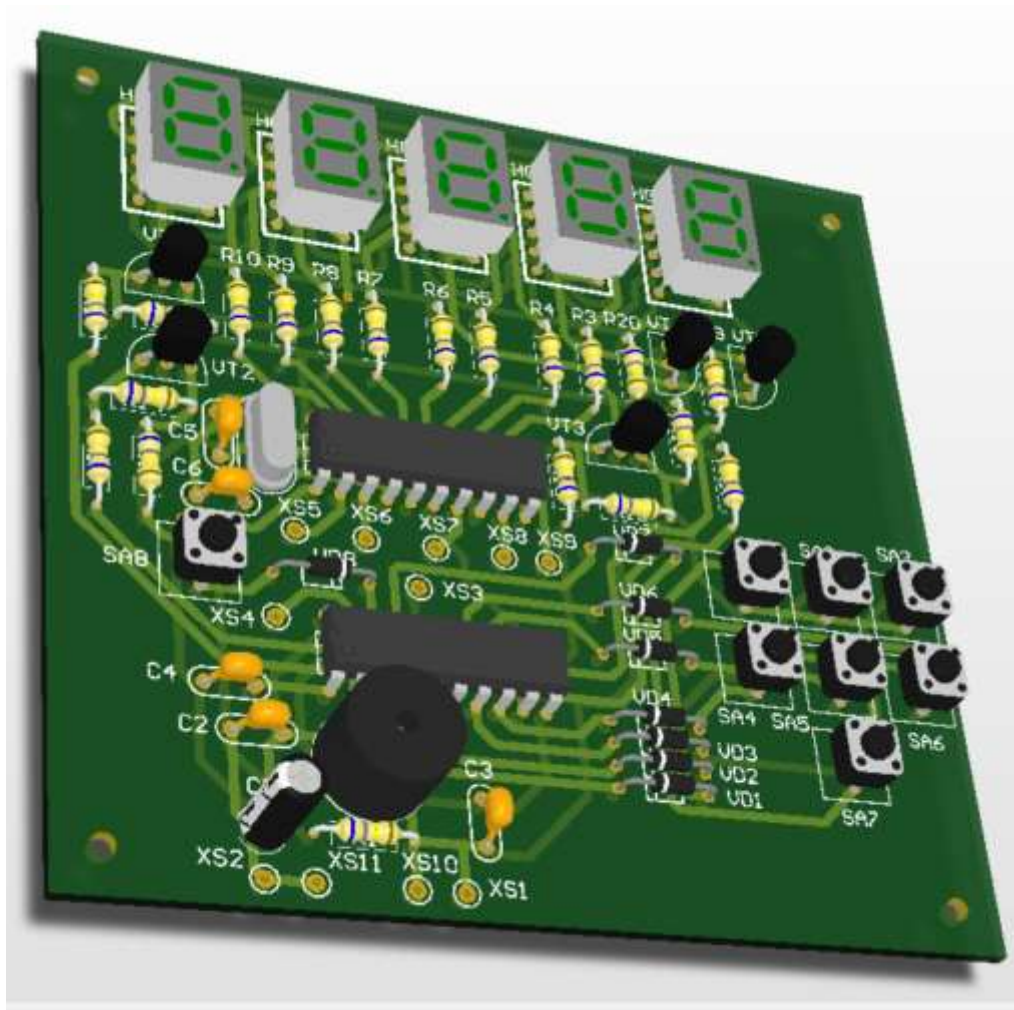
3D модель друкованого вузла, вигляд зверху
